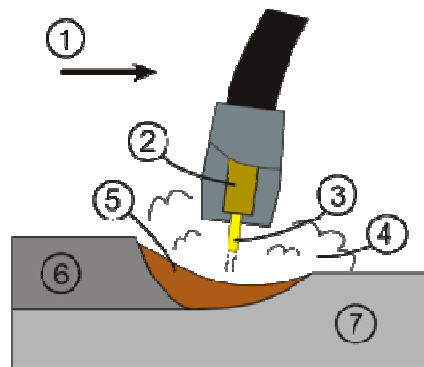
(GMAW) Área de soldado. (1) Dirección de avance, (2) Tubo de contacto, (3) Electrodo, (4) Gas (5) Metal derretido de soldadura, (6) Metal de soldadura solidificado, (7) Pieza a soldar.
